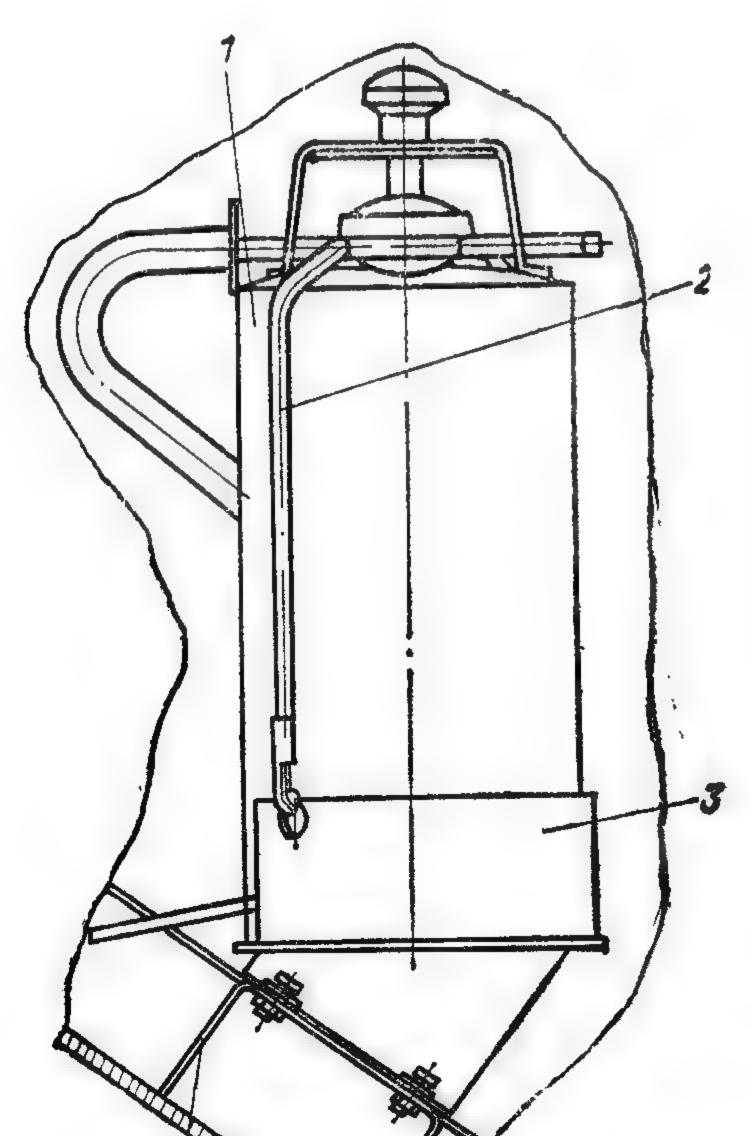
Установка нагнетателя для масла: 1 — нагнетатель; 2 — шнур резиновый; 3 — гнездо; 4 — крокштейн
